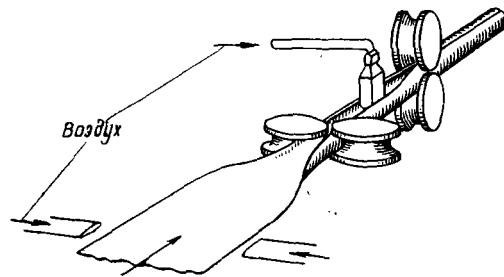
Принципиальная схема непрерывной печной сварки труб встык
